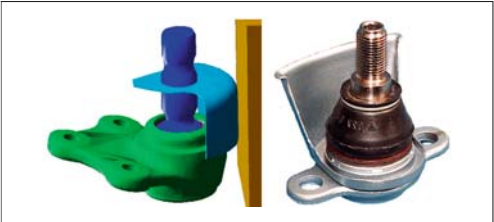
Führungsgelenke, Gehäusevarianten [66]
